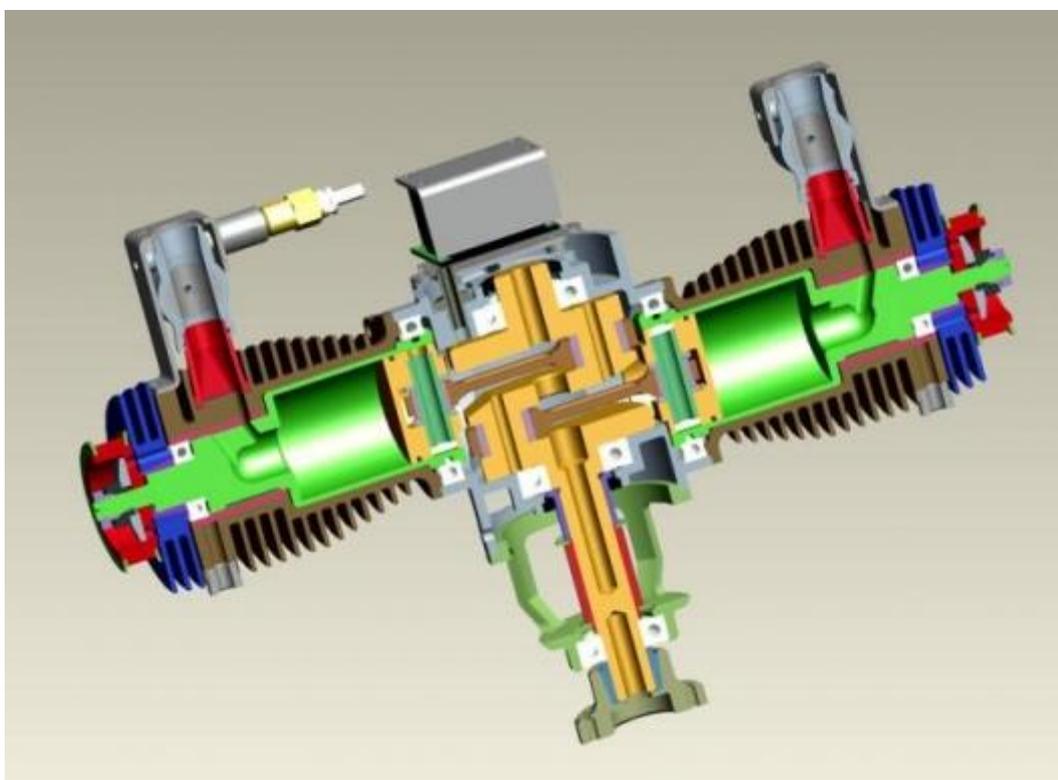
Авиамодельный оппозитный двигатель первых серий с вращающимися гильзами.
